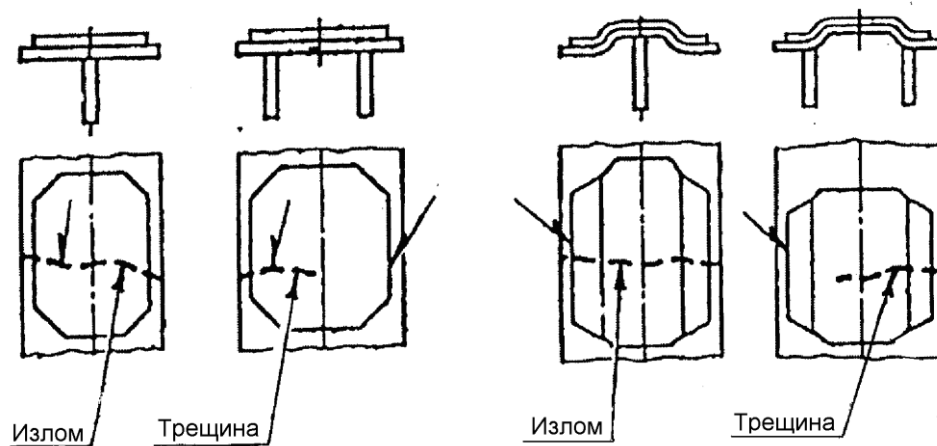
Верхние листы промежуточной и шкворневой балок, отремонтированные сваркой
